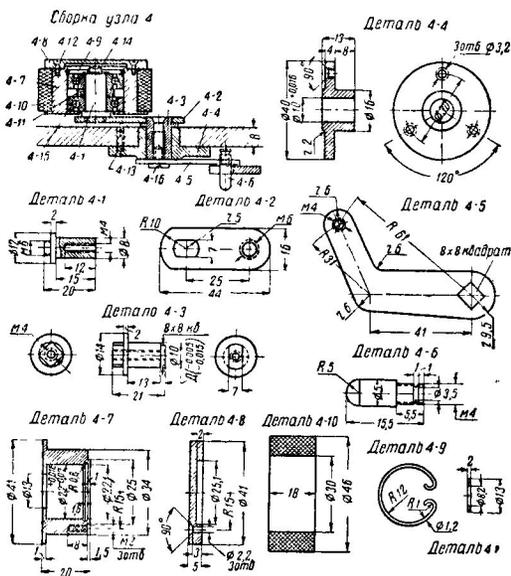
Прижимной ролик (узел 4) и его детали: 4-1 — ось ролика (сталь 45) — 1 шт.; 4-2 — малый рычаг (сталь 20-листовая толщиной 2 мм) — 1 шт.; 4-3 — ось рычага (сталь 45) — 1 шт.; 4-4 — подшипник (сталь 25) — 1 шт.; 4-5 — большой рычаг (сталь 20-листовая толщиной 2 мм) — 1 шт.; 4-6 — палец (сталь У8А) — 1 шт.; 4-7 — стакан (сталь 25) — 1 шт.; 4-8 — крышка (сталь 25) — 1 шт.; 4-9 — опорное кольцо (пруж. сталь марки Н) — 1 шт.; 4-10 — кольцо (резина средней твердости) — 1 шт.; 4-11 — распорное кольцо (сталь 3) — 1 шт.; 4-12 — винт М2 × 8 мм (сталь 3) — 3 шт.; 4-13 — винт М3 × 10 мм (сталь 3) — 3 шт.; 4-14 — винт М4 × 8 мм (сталь 3) — 1 шт.; 4-15 — шарикоподшипник с внешним диаметром 22 мм, внутренним — 8 мм и высотой 7 мм — 2 шт.; 4-16 — винт М4 × 10 мм (сталь 3) — 1 шт. Диаметр оси 4-1 (8 мм) должен быть подогнан под внутренний диаметр шарикоподшипника 4-15 в расчете на скользящую посадку
